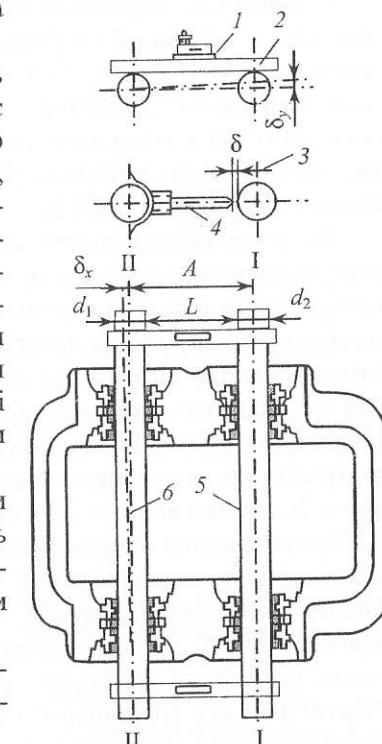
Центрування осей редуктора за контрольними валами:
